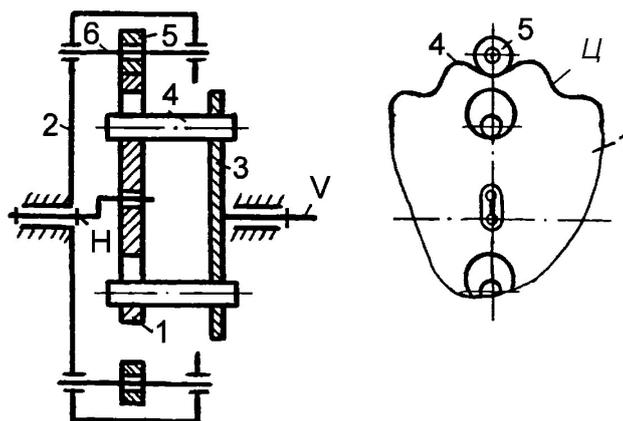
Планетарно-цевочный редуктор схемы $K-H-V$
